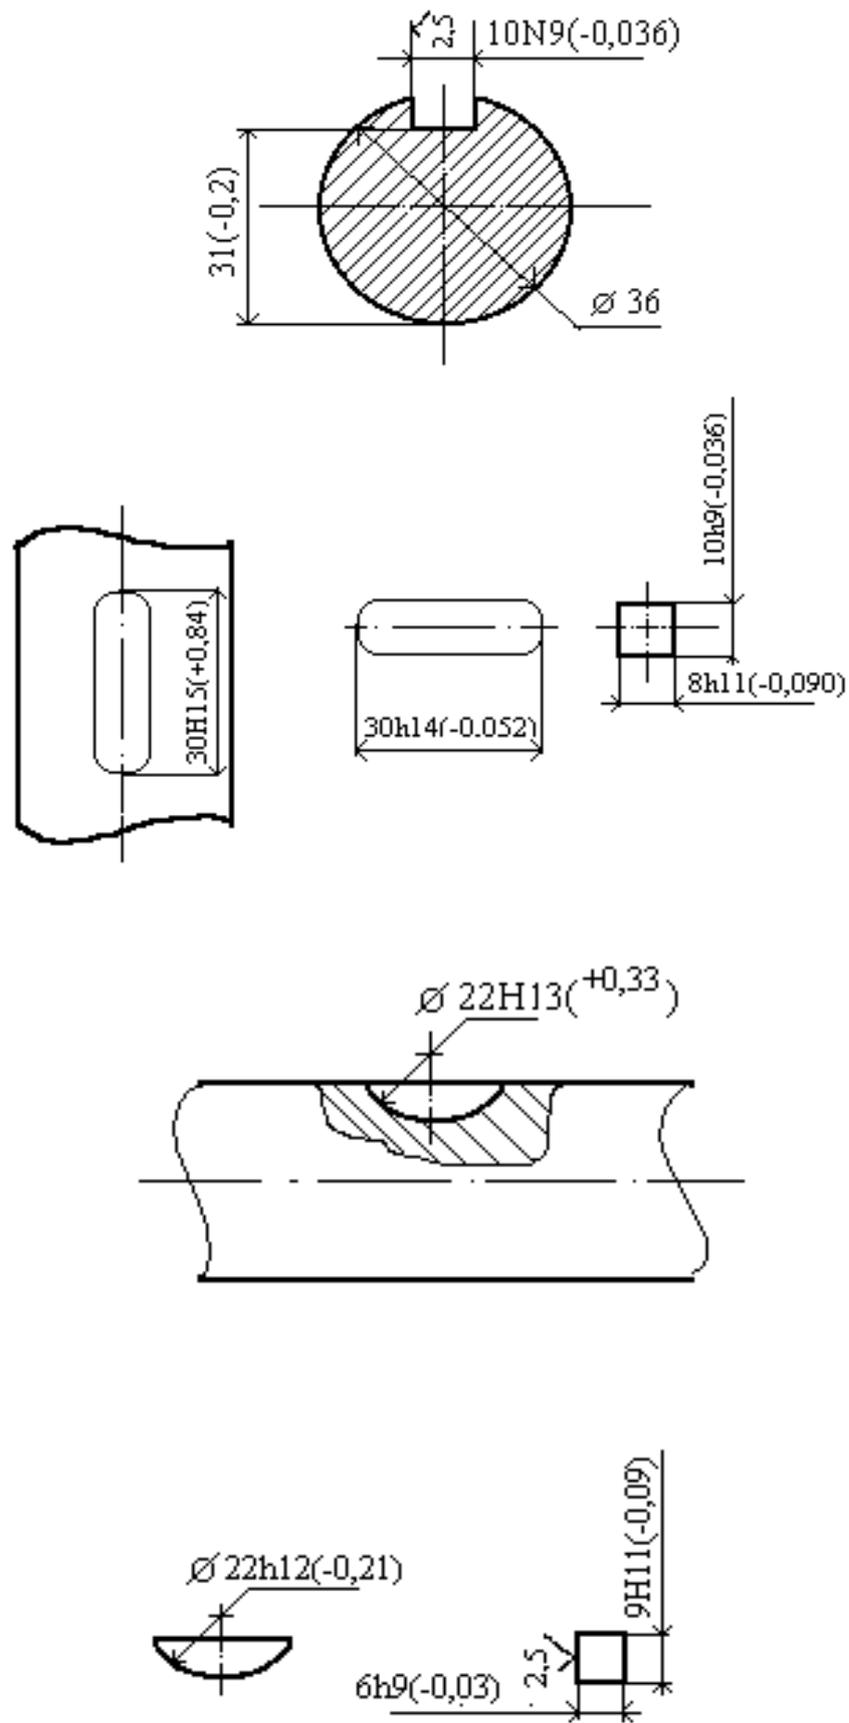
Эскизы деталей шпоночного соединения
